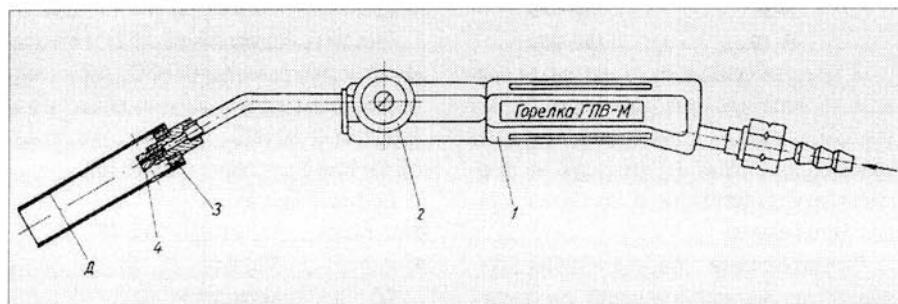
Горелка для пайки деталей из стали и цветных сплавов:
